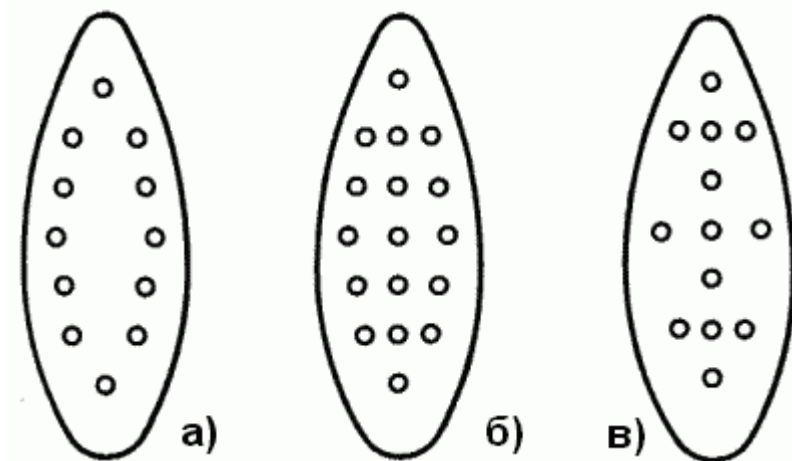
Установка заклепок или стержней одного металла в заготовку другого: – варианты расположения заклепок или стержней в блесне
